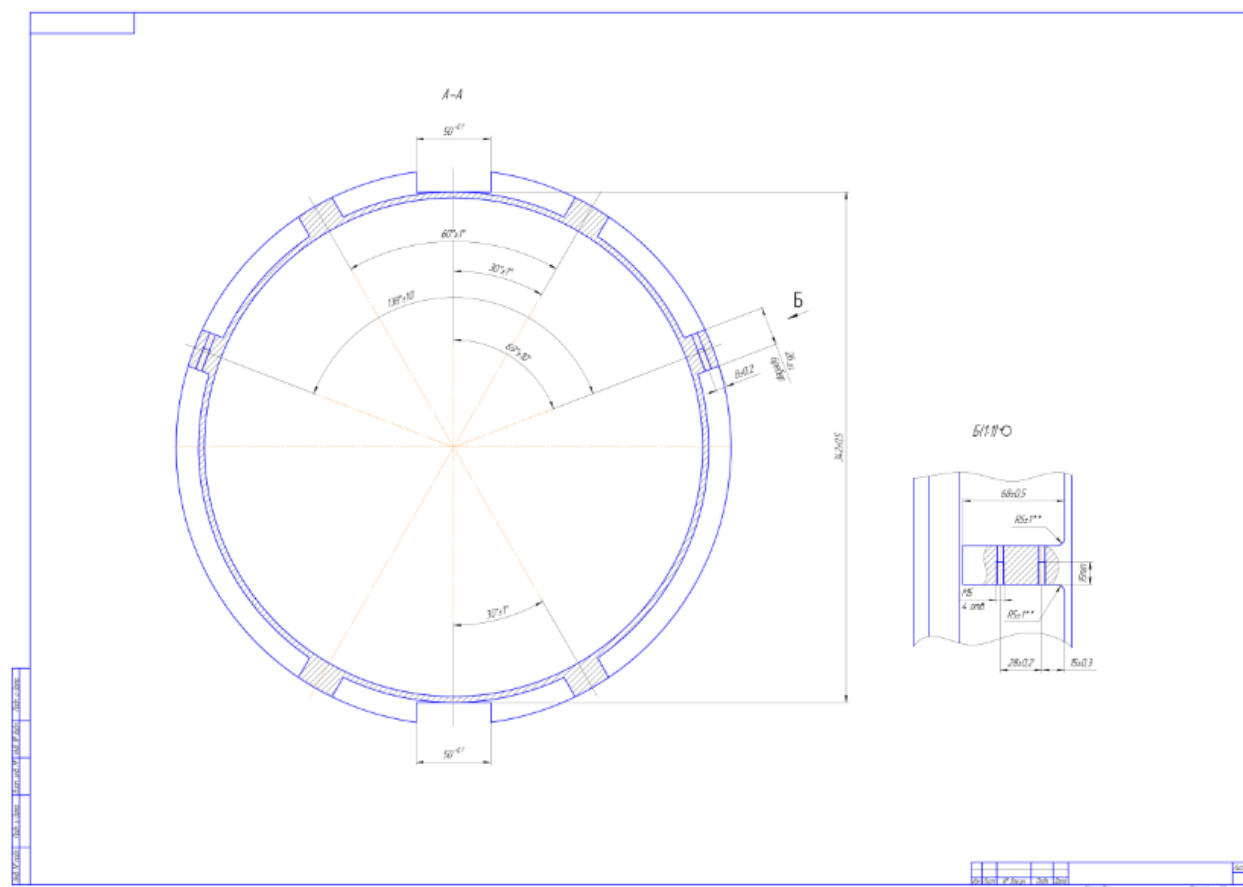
Чертеж детали «Корпус» сечение А-А
